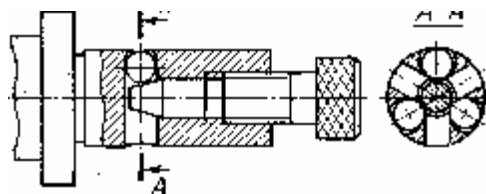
Схема пристрою з розтискними кульками для вибірки радіальних зазорів
